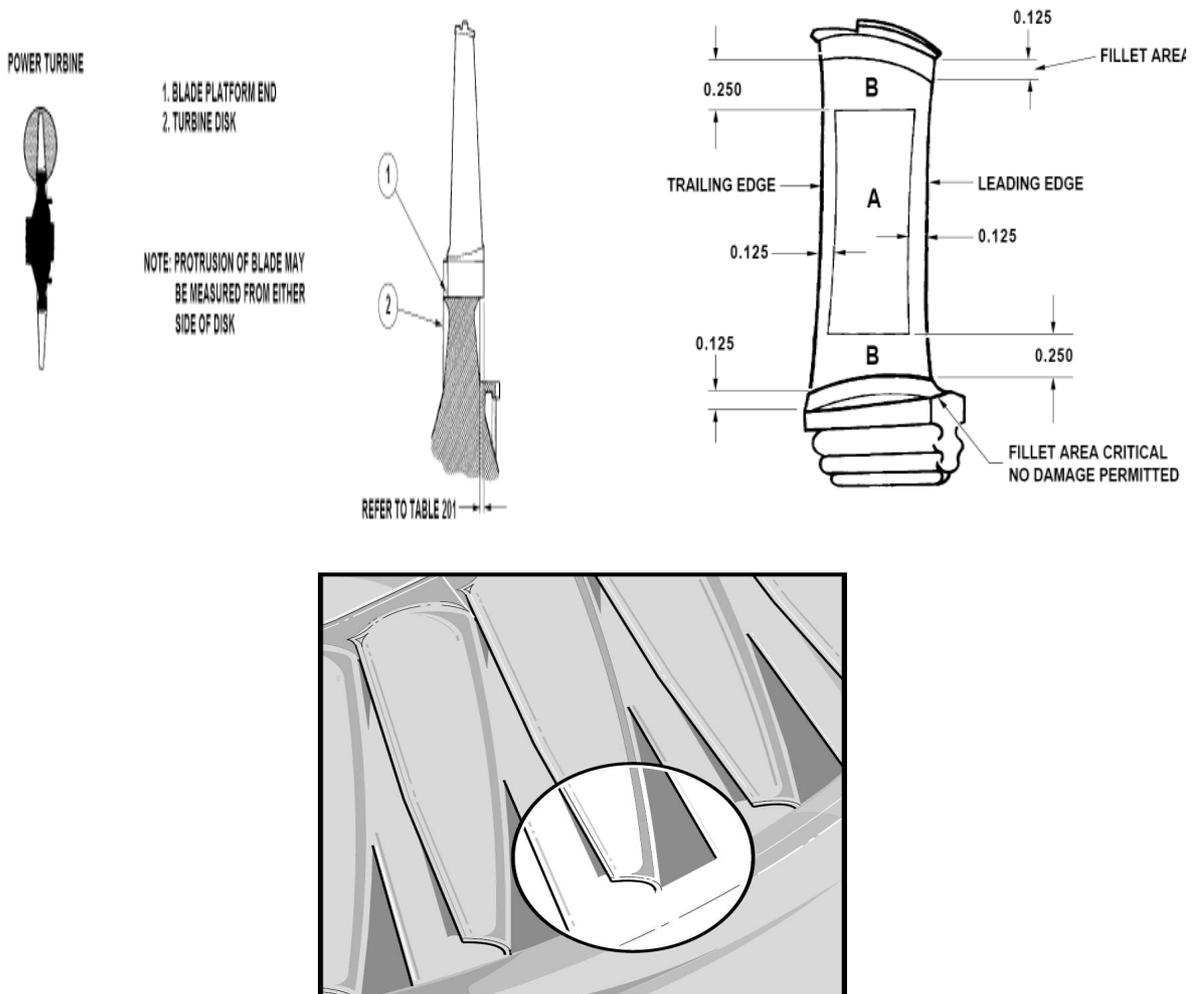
inspection d'ailette rotor de la turbine libre
